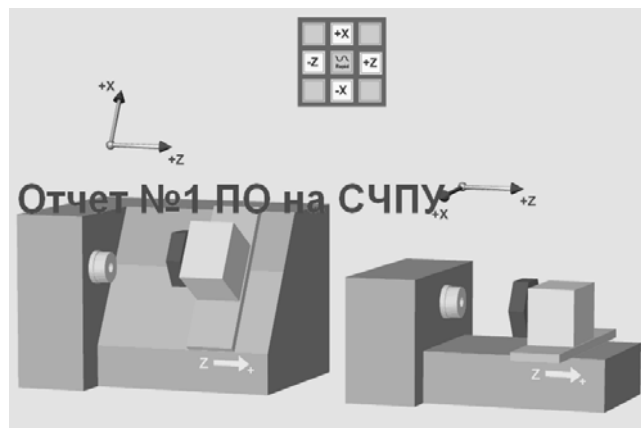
Система координат токарного станка с ЧПУ
